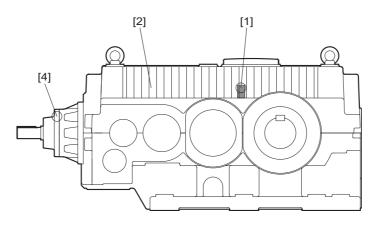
M4R.. Posiciones de montaje de los adaptadores SPM
